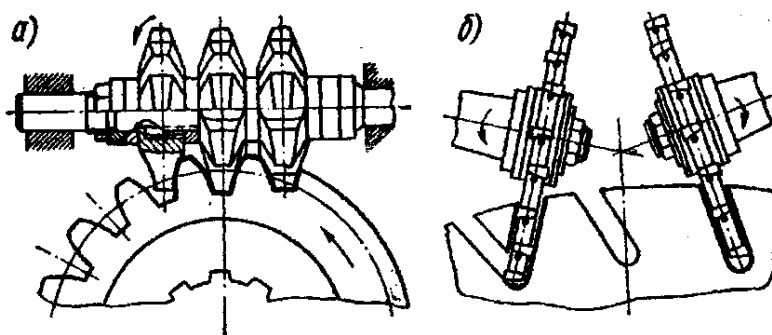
Нарезание зубьев зубчатых колес дисковыми фрезами: *а* – тремя дисковыми угловыми фрезами; *б* – двумя специальными дисковыми фрезами
